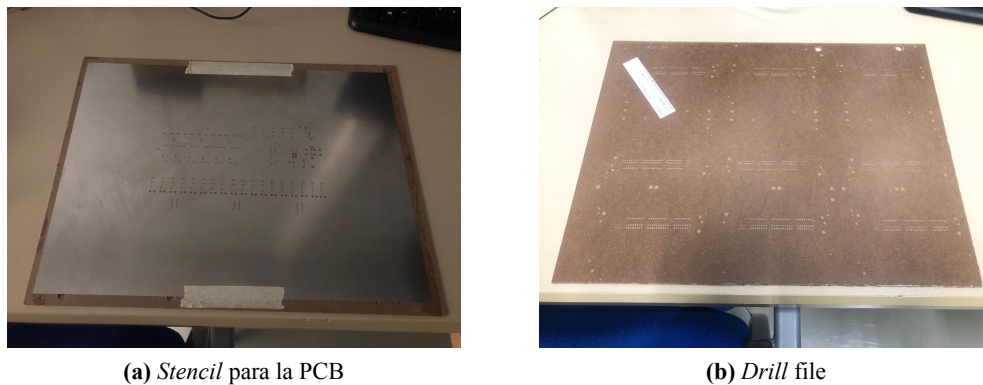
Stencil y drill files para la soldadura de componentes en PCB. Fuente: propia
